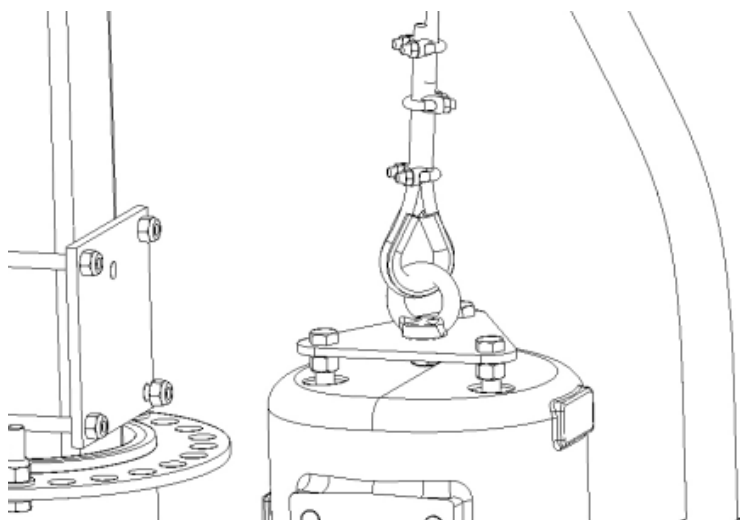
Montage mittels Seilkausche und Ringschraube
